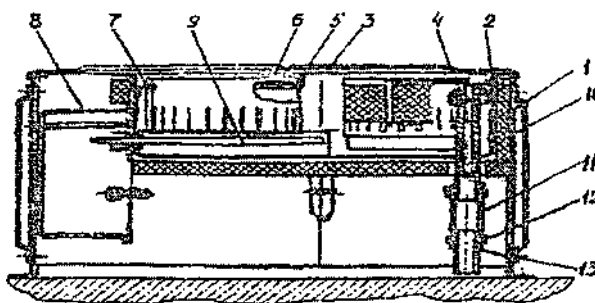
Автонапувалка АГК - 4Б 1 - корпус; 2, 5 - чаша; 3 - кришка; 4 - клапанний механізм; 6 - поплавок; 7 - терморегулятор; 8 - шафа керування; 9 - електронагрівач; 10 - плити; 11 - рукав; 12 - хомут
